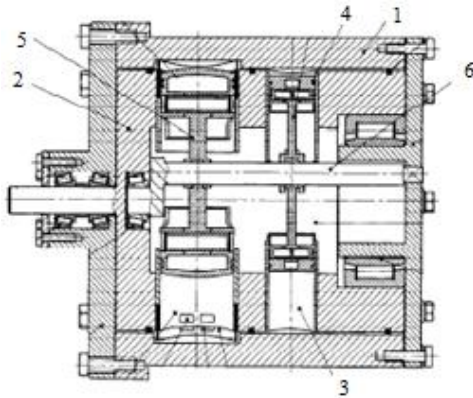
Конструктивна схема роторно-поршневого двигуна [4]: 1 – корпус; 2 – ротор; 3 – циліндр; 4 – поршень; 5 – шатун; 6 – колінчатий вал
